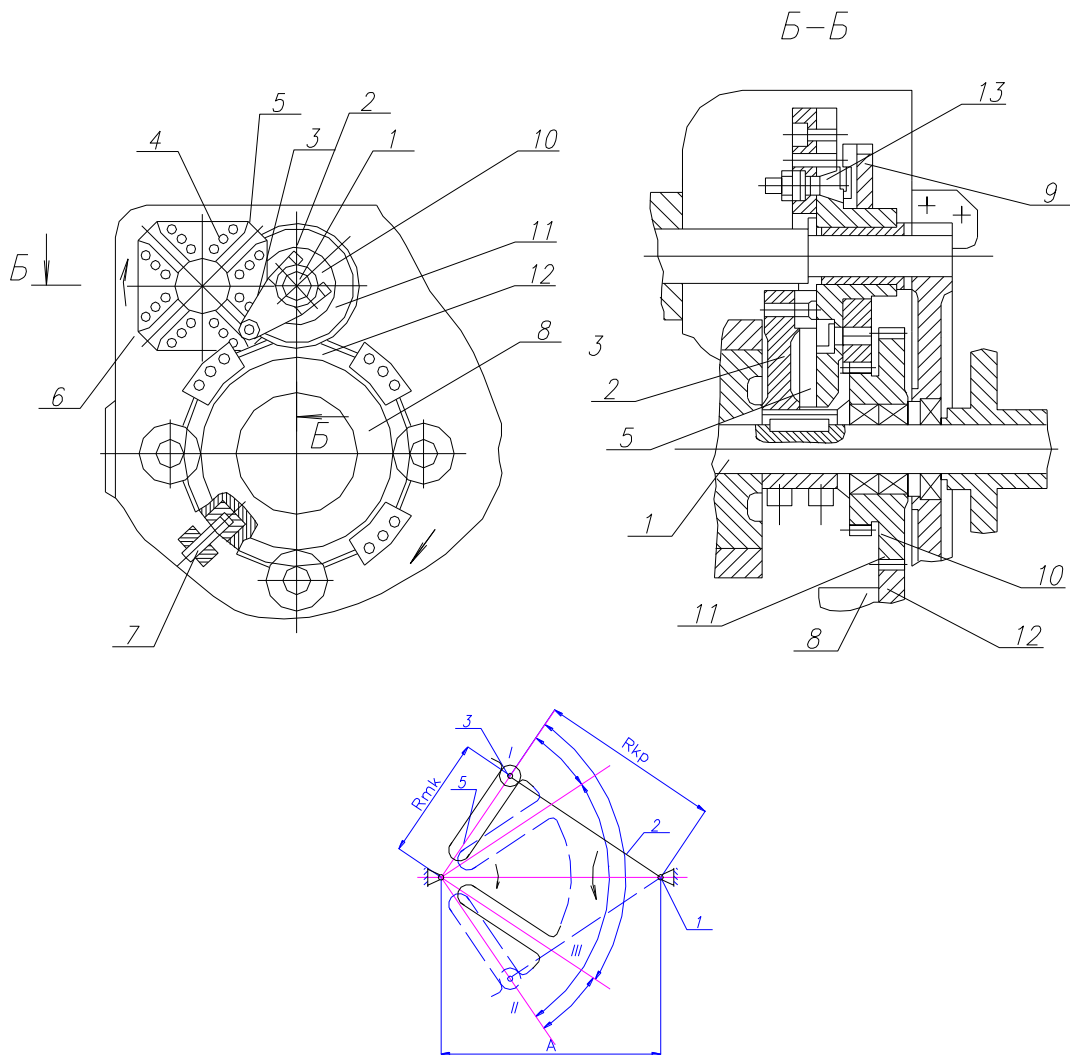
Загальний вид механізму (а); (б) - розріз Б-Б; (в) - схема механізму, яка показує взаємодію пальця кривошипа і хреста
